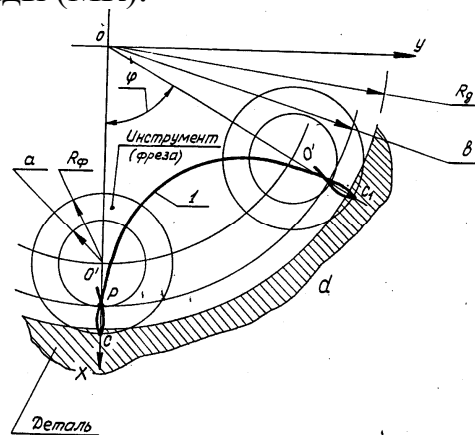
Схема планетарного формообразующего движения инструмента относительно оси.
